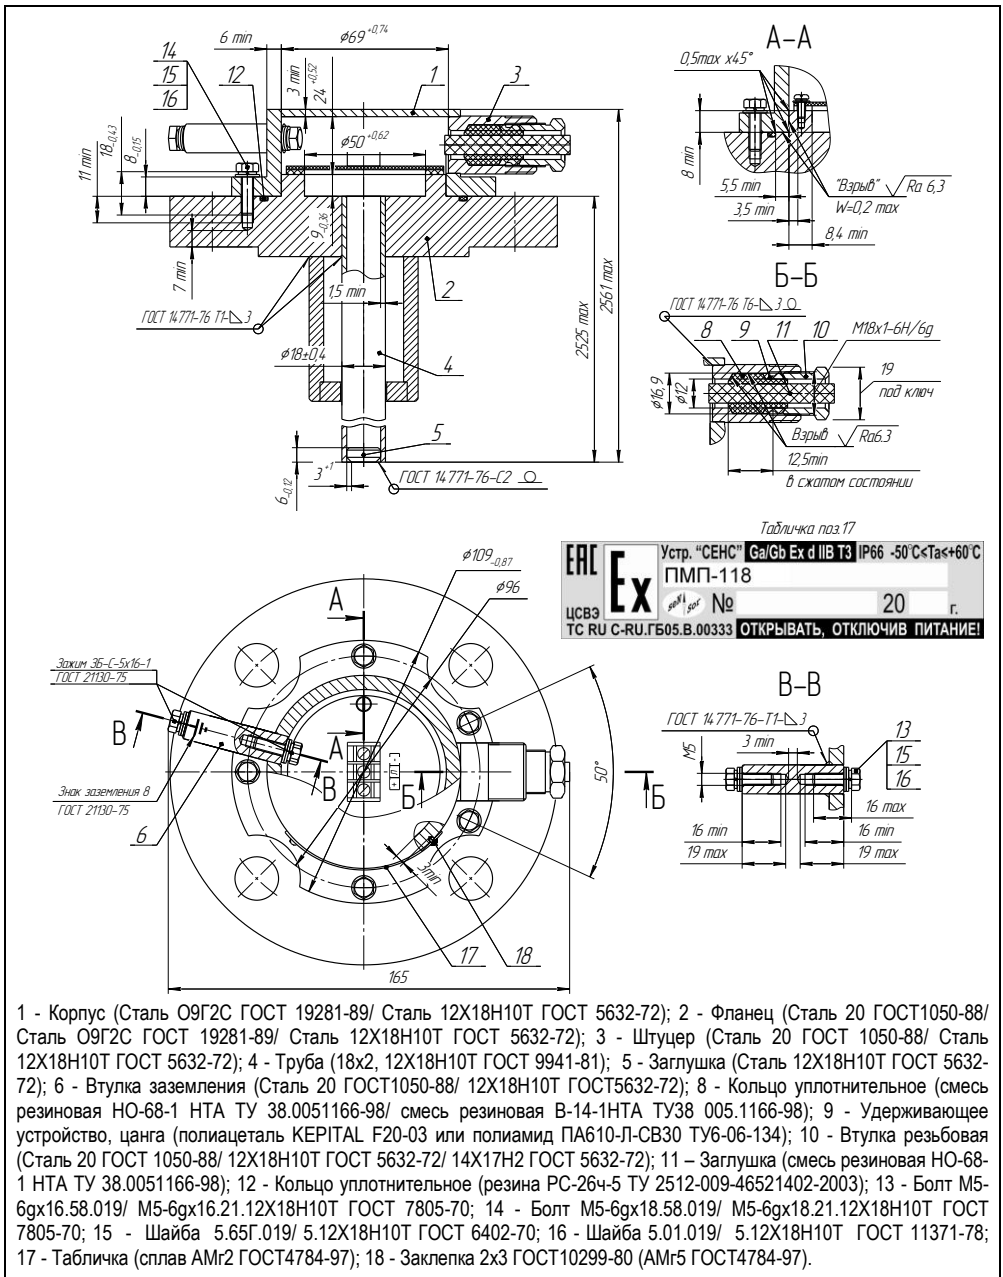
Чертеж средств взрывозащиты для преобразователя с корпусом hk36
